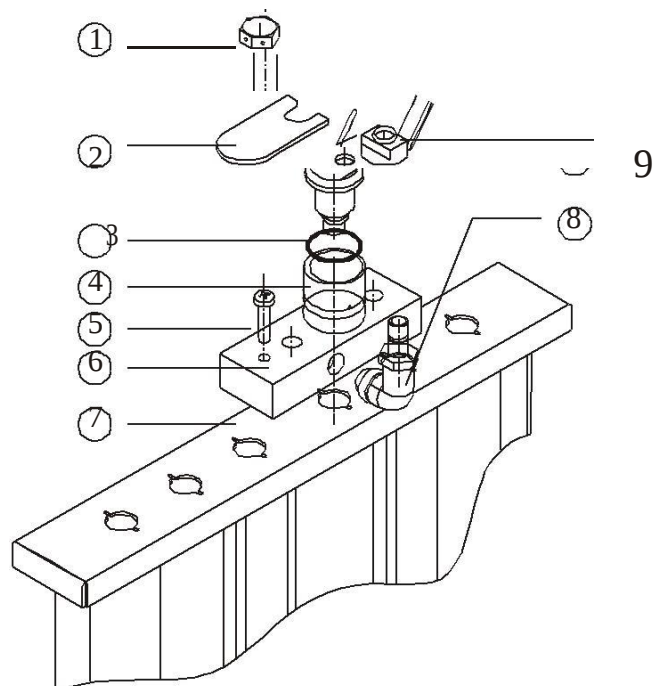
Схема установки инжектора с боковой подачей топлива
